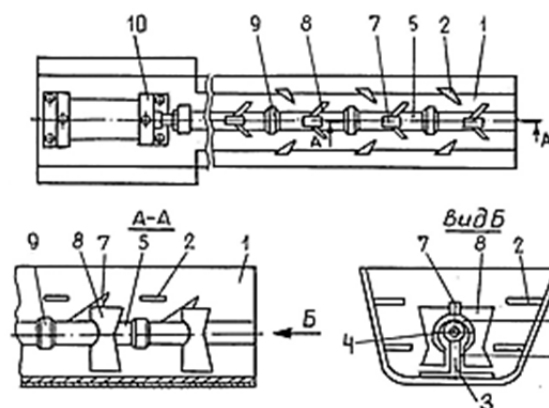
Фрагмент штангового конвейера (вид сверху)
